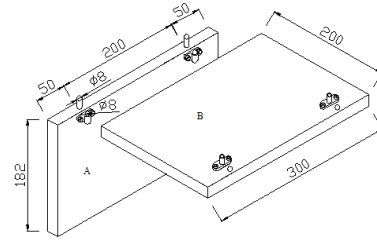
Kınışlı-lambalı birleştirme (Barefaced housing joint) (size in mm)
